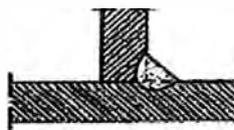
Junta de filete con soldadura de un lado
